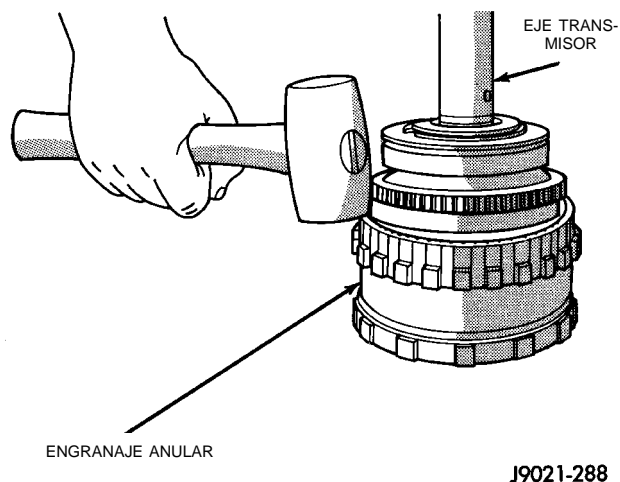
Desmontaje del anillo de muelle del engranaje anular
